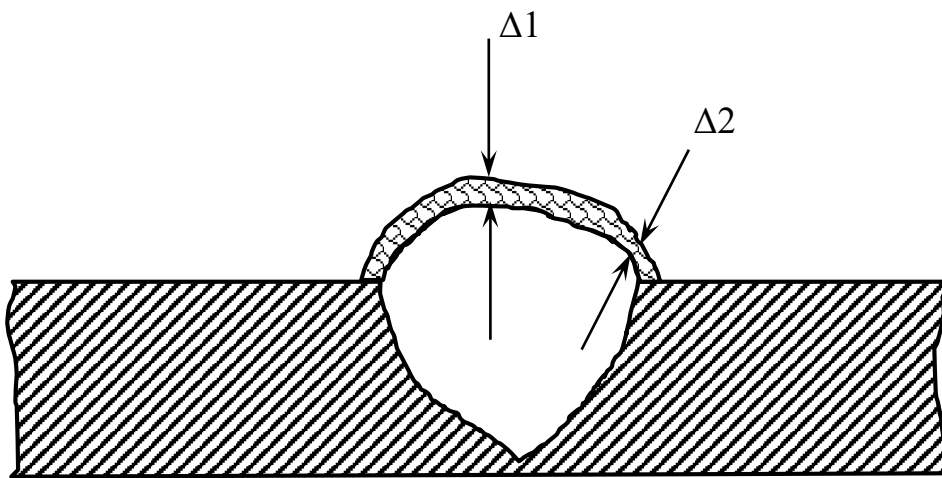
Схема вимірювання товщини шлакової кірки
